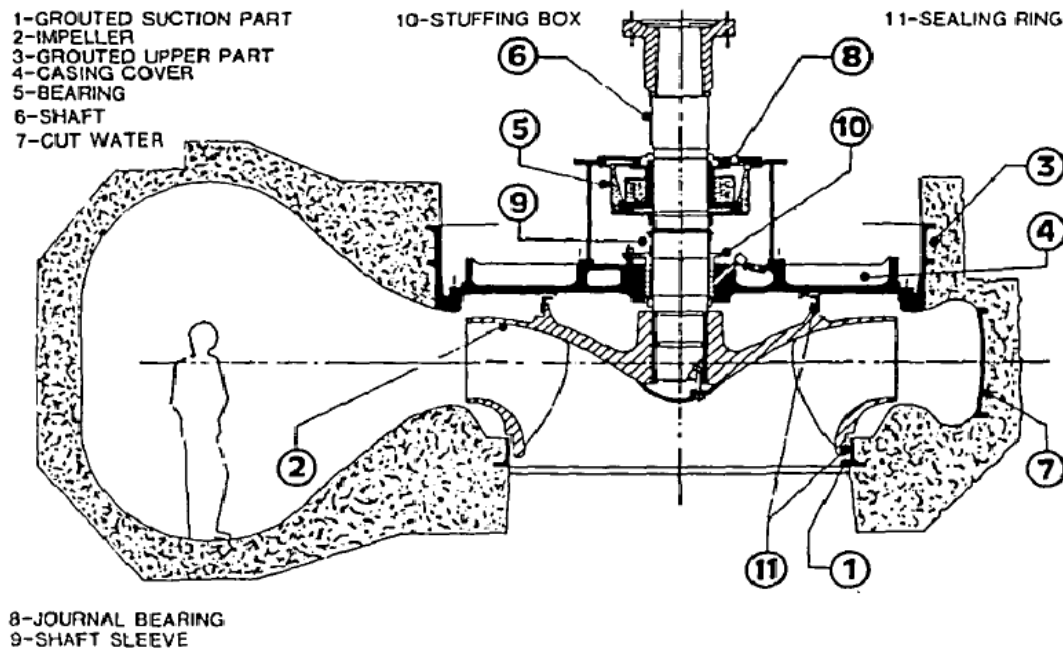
Layout Betonspiralgehäusepumpe [5]
